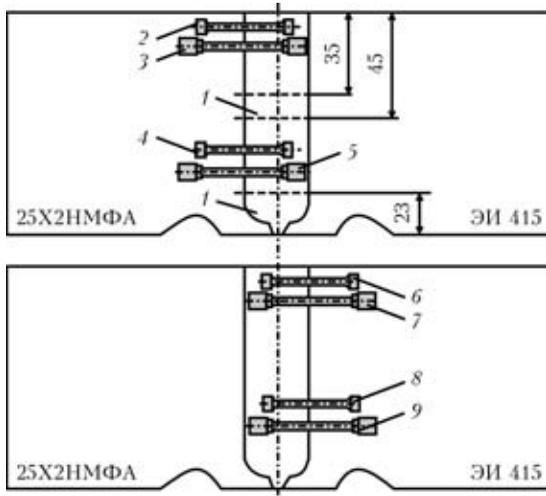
Расположение зон шва по высоте поперечного сечения комбинированного сварного соединения и схема вырезки образцов для испытания на растяжение (обозначения см. в тексте)
